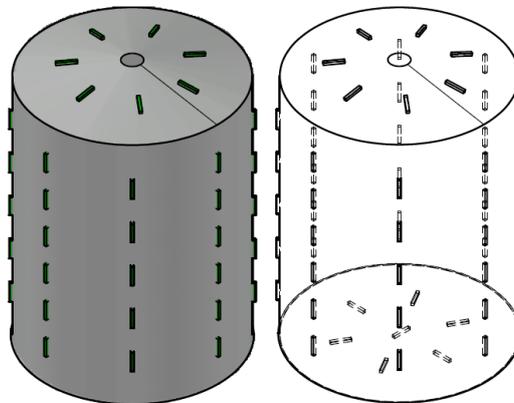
Detail desain gambar kerja pada *tank Shell
